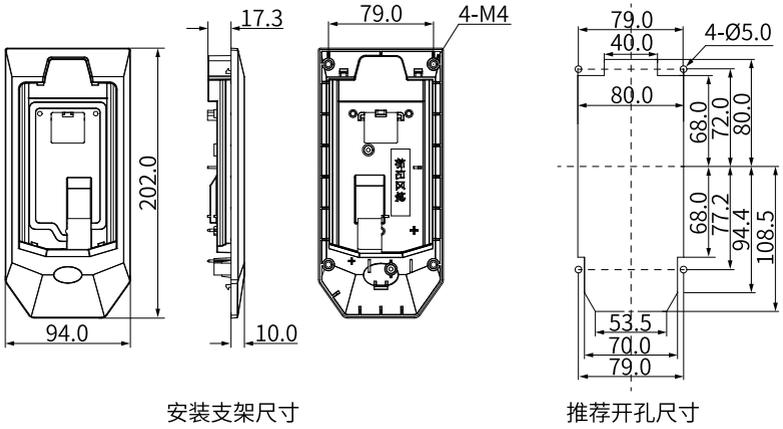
SOP-20-810外引操作面板安装支架尺寸及开孔尺寸 (单位: mm)
